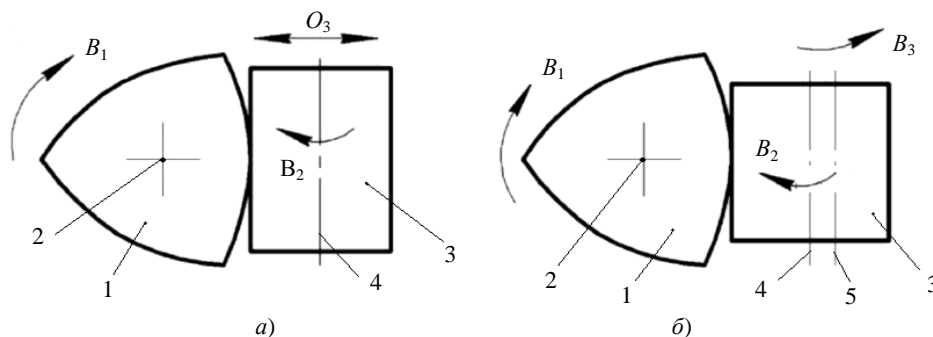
Схемы обработки некруглых поверхностей с разделенными движениями профилирования и резания при сообщении режущему инструменту дополнительного осциллирующего движения (а) или вращательного движения (б)
